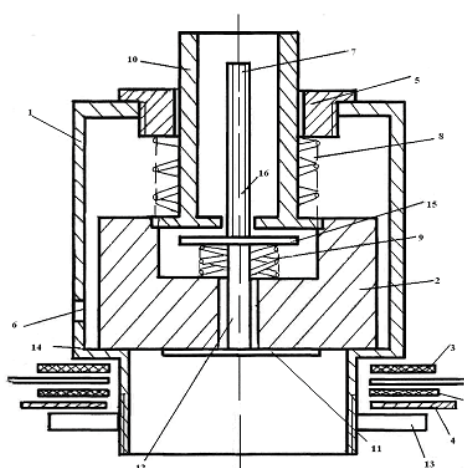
Комбинированный клапан для регулирования газовой среды: 1 - корпус; 2 – поршень; 3 - резиновые уплотнители; 4-шайбы; 5- регулировочная гайка; 6 - сбросное отверстие; 7 – шток; 8 – пружина; 9 -возвратная пружина; 10 - штуцер; 11 - клапан; 12 – впускное отверстие; 13 - гайка; 14 – посадочное место; 15 -регулировочная шайба; 16 – резьба [25].
